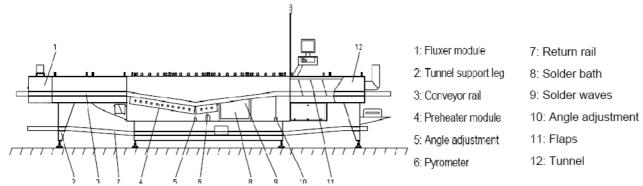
Máquina de soldadura por onda EPM - Adaptado do manual da máquina
